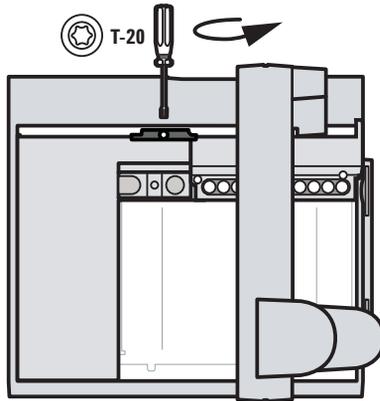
Entfernen der T-20-Schraube aus der Transportklammer
